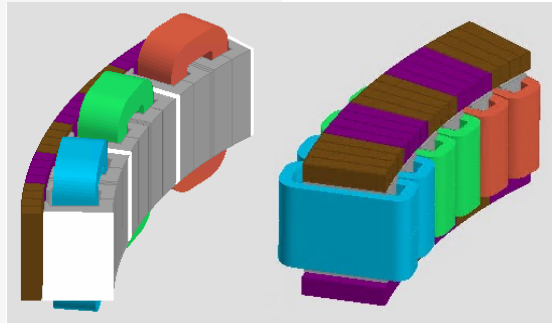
Links: Endgültige RFPM-Maschine; Rechts: Endgültige AFPM-Maschine.
